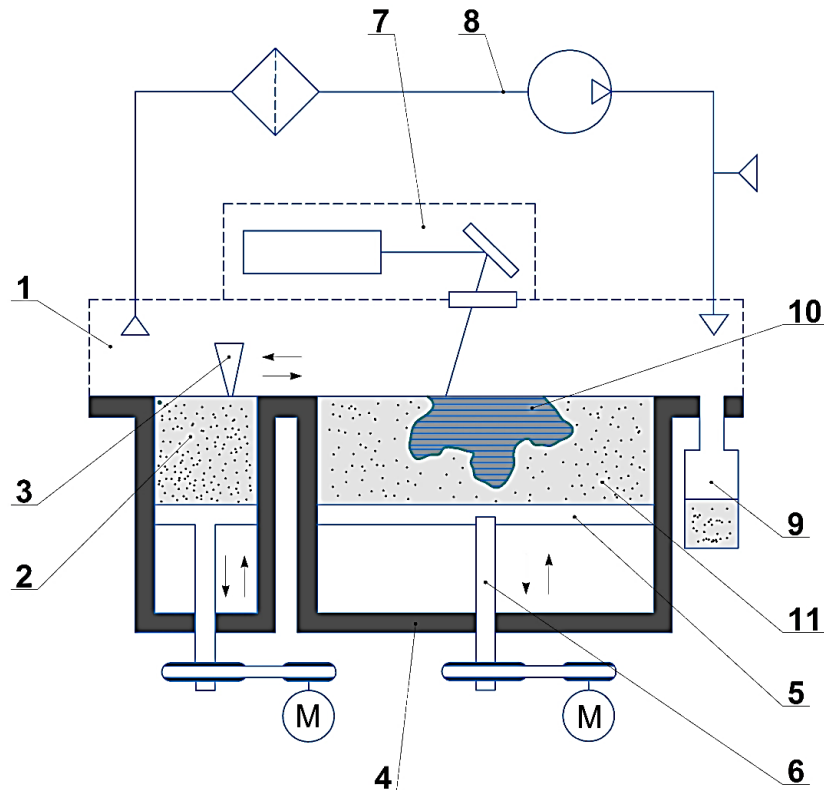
Кінематична схема СЛС: 1 – робоча камера; 2 – пристрій дозування порошку; 3 – пристрій розрівнювання порошку; 4 – колодязь побудови; 5 – платформа побудови; 6 – механізм вертикального переміщення платформи побудови; 7 – лазерна оптична система; 8 – система формування захисної атмосфери; 9 – система накопичення надлишкового порошку; 10 – деталь; 11 – порошок
